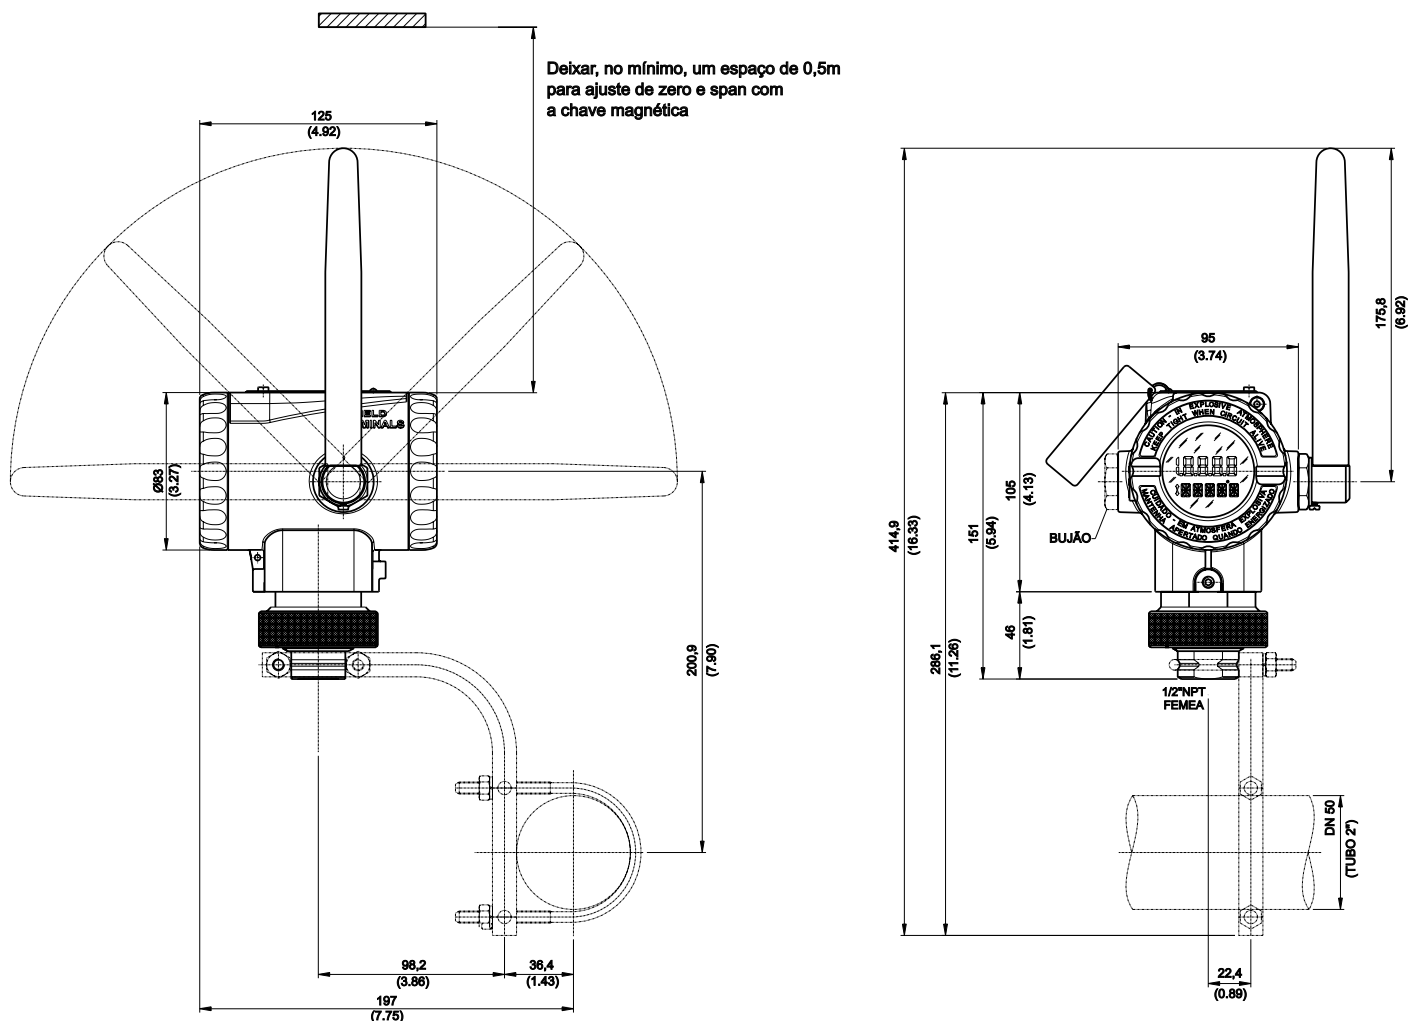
Desenho Dimensional do TT400 WirelessHART™
